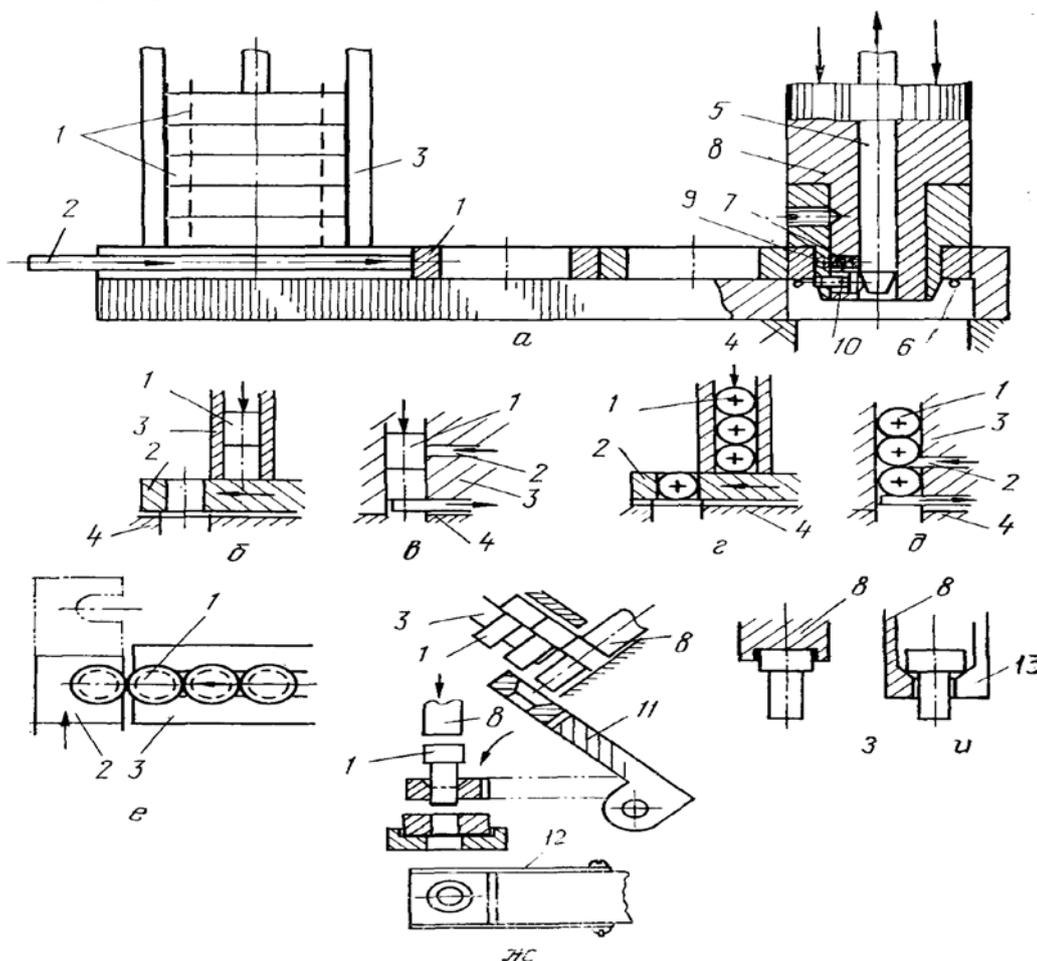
Установка присоединяемых деталей по цилиндрическим поверхностям
